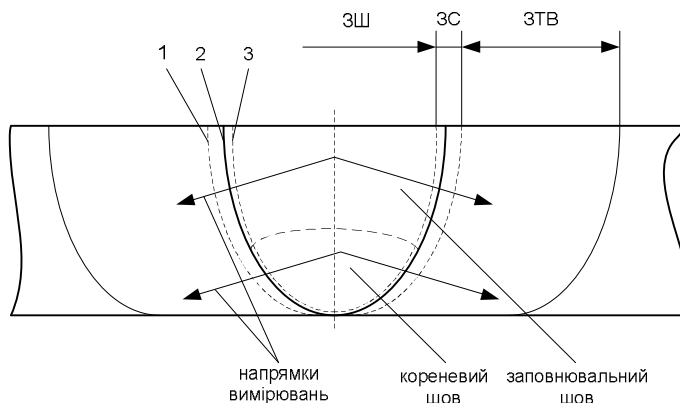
Схема проведення вимірювань: 1 – ділянка неповного розплавлення металу з'єднання;
